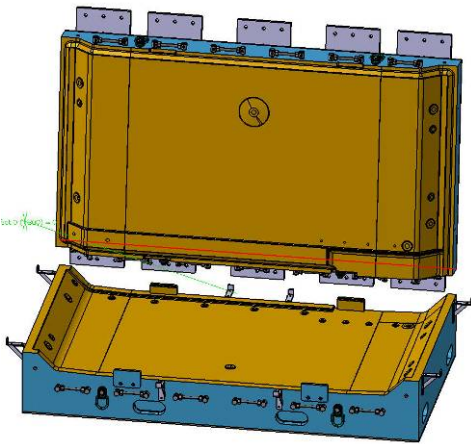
Werkzeug Bodenplatte 3 (CAD)
